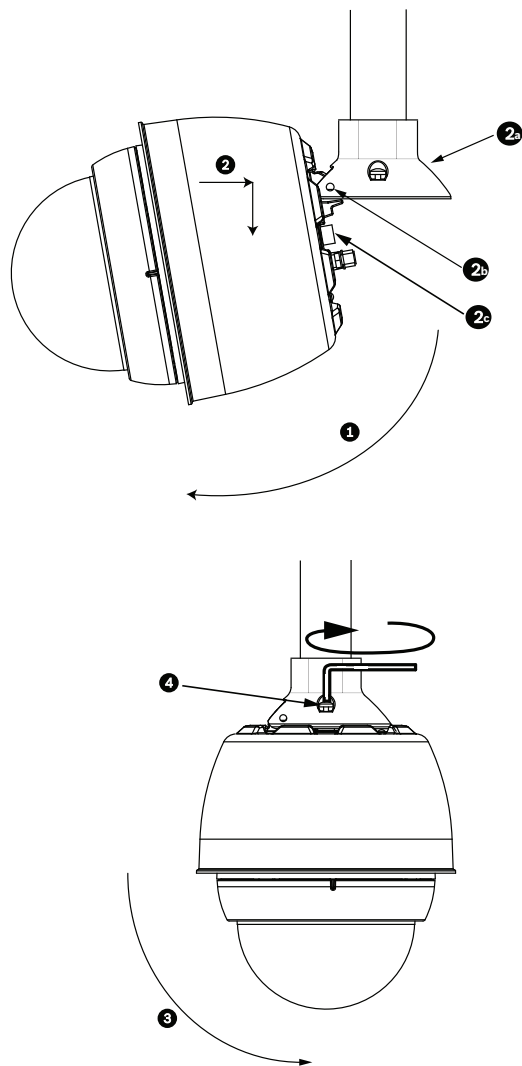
Instalação do elemento pendente no suporte de telhado/tubo
